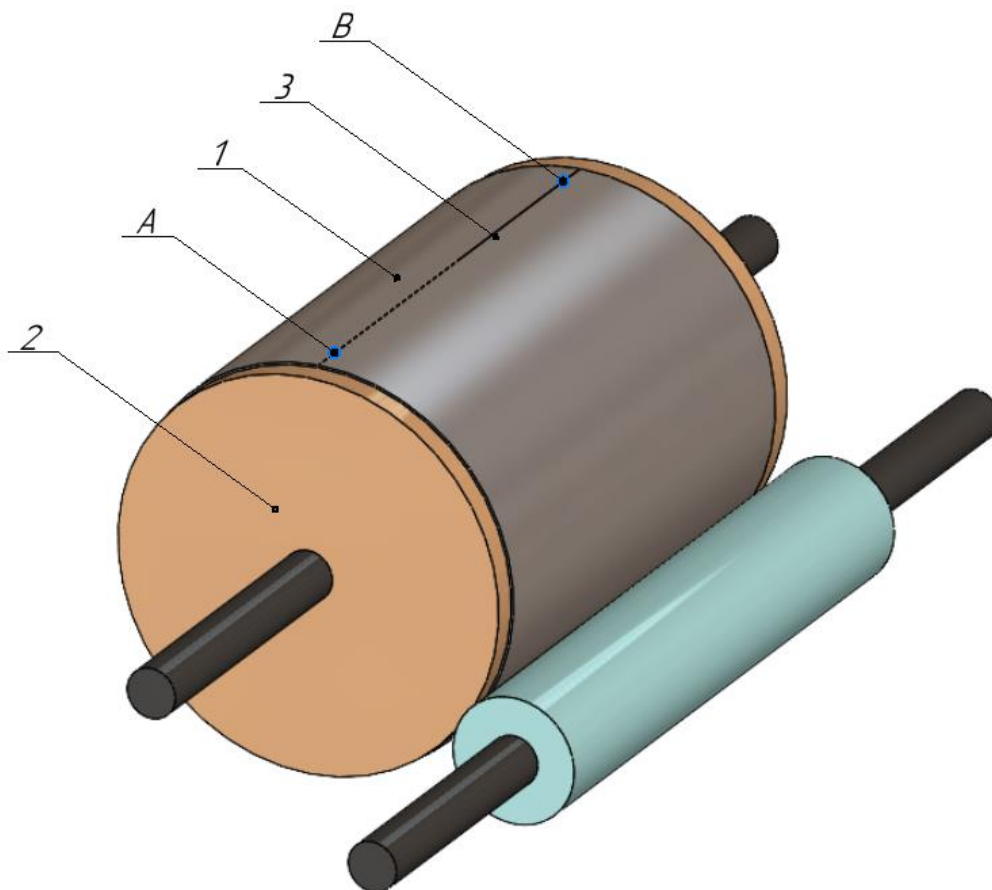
Эскиз рабочей части технологического оборудования для формирования цилиндрической оболочки: 1 – заготовка цилиндрической оболочки, 2 – технологическая оснастка, А, В – точки сварки, для сохранения полученной формы, 3 – контур внешнего стыкового сварочного шва
